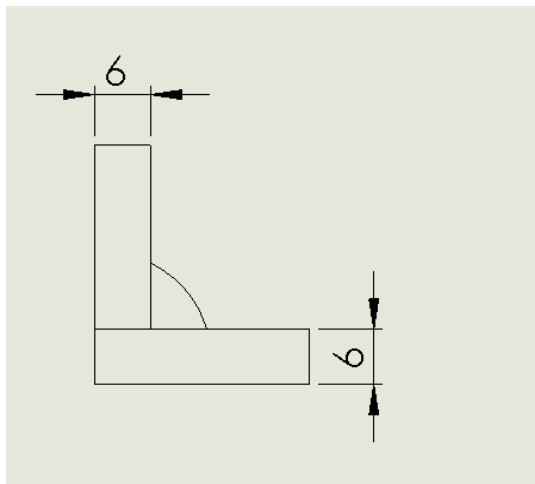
Diseño de junta soldada para placas de 6 mm. Fuente:
